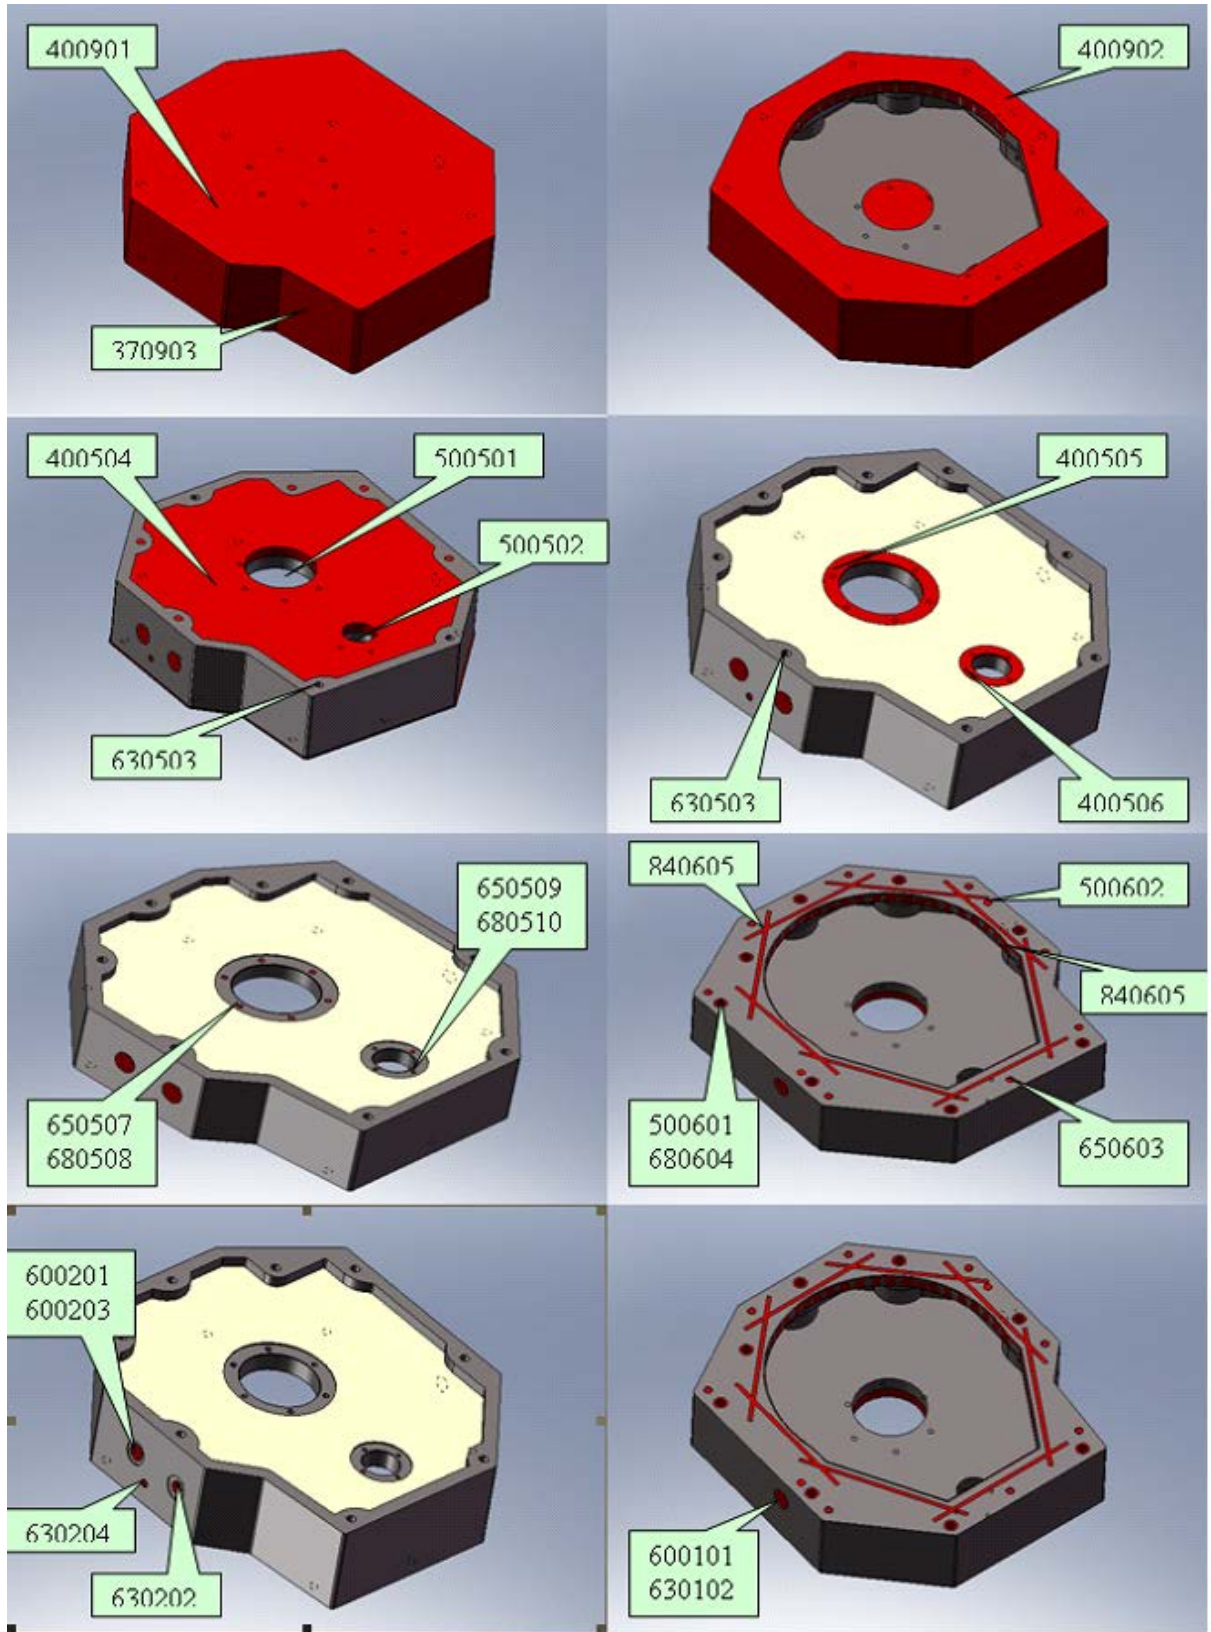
Кодування поверхонь деталі типу «Корпус».
